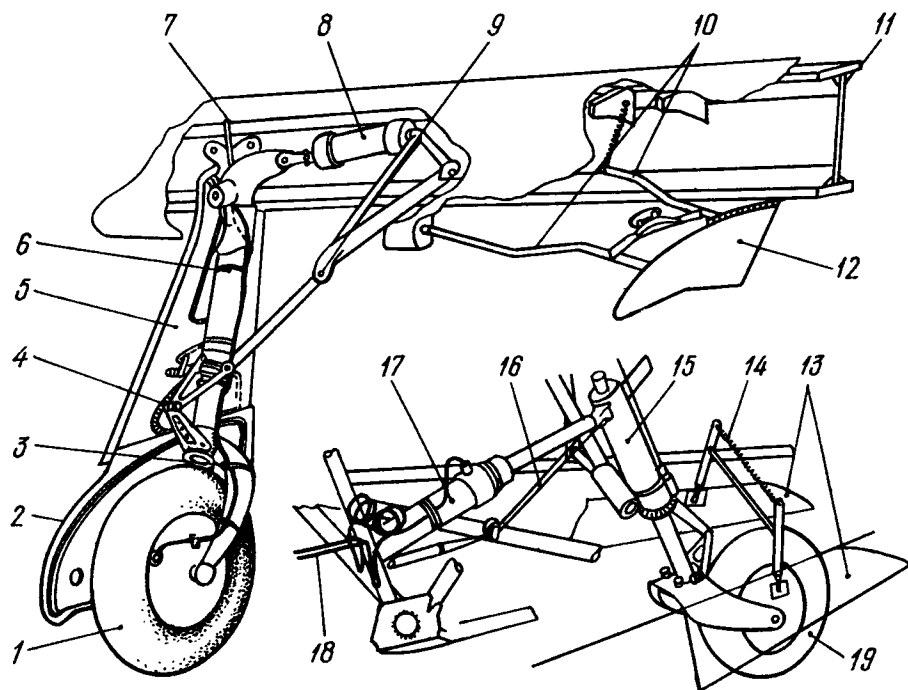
Конструктивная схема убирающегося основного шасси и хвостового колеса истребителя Як-9:
